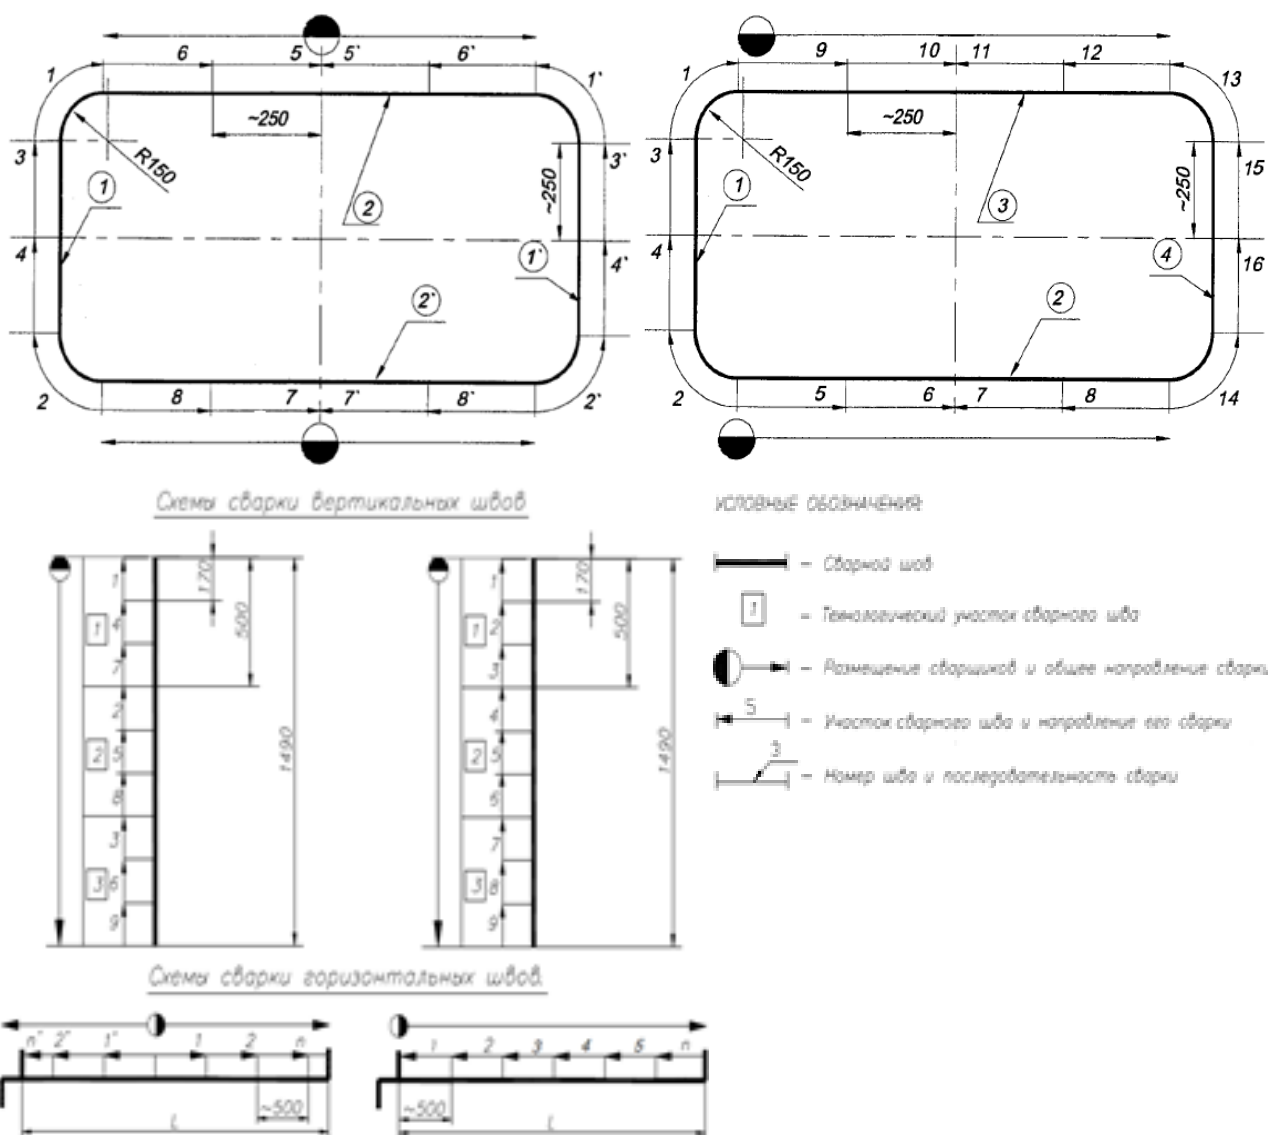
Схема сварки ремонтной листовой вставки
